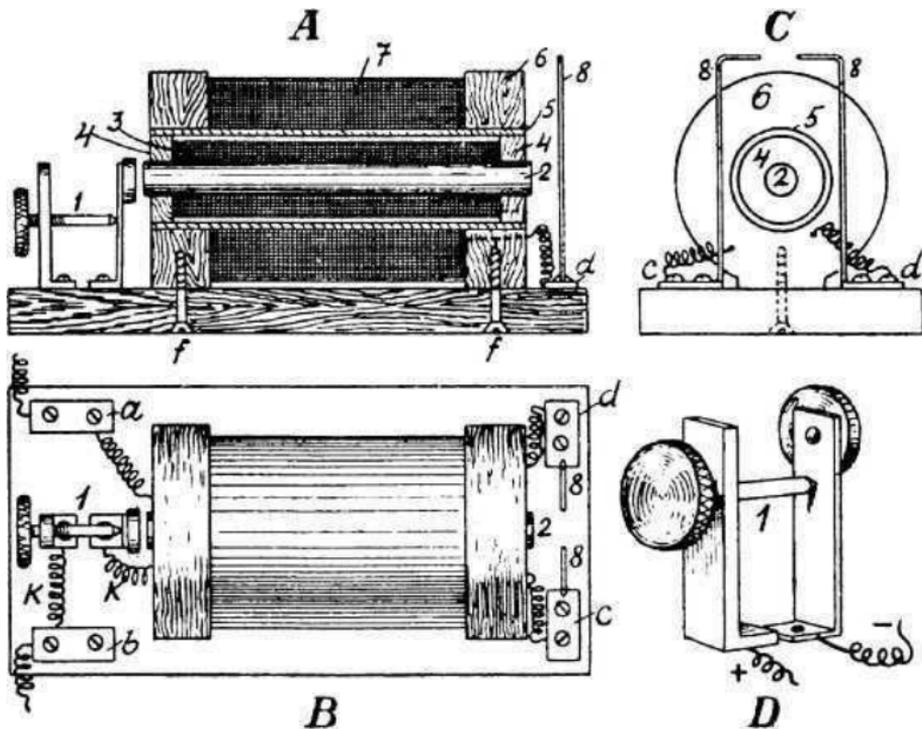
А – разрез, В – вид сверху, С – вид сбоку, D – прерыватель
